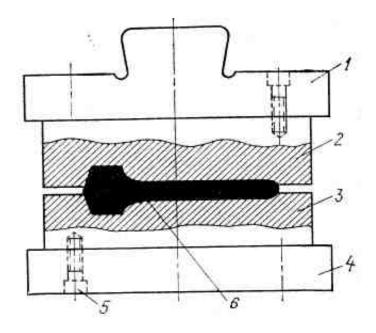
Схема штампа для правки: 1 – верхний блок; 2, 3 – рабочие вставки; 4 – нижний блок; 5 – болт; 6 – поковка
